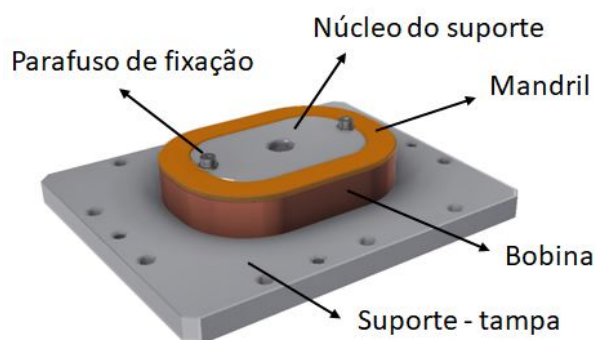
Representação do desenho técnico do conjunto para bobinagem: mandril, núcleo e suporte. Fonte: adaptado de [\[19\]](#)
